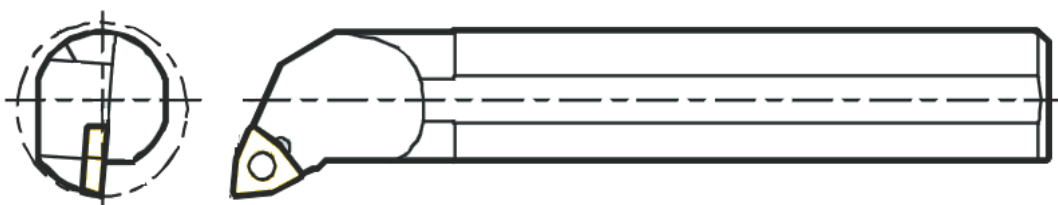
Розточний різець фірми Kovel tools, S25R-SWLCR/L-08
